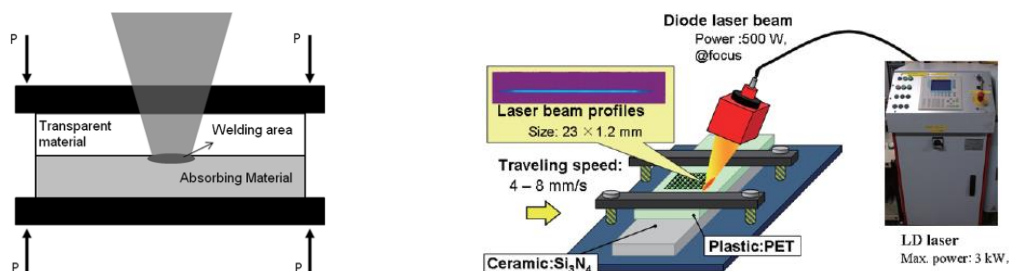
Principe du soudage laser par transmission [63] et application à l'assemblage polymère-métal [64]
